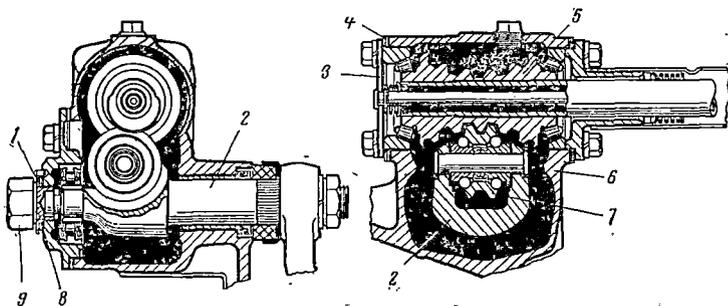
Схема устройства рулевого механизма автомобиля ГАЗ-51А:
